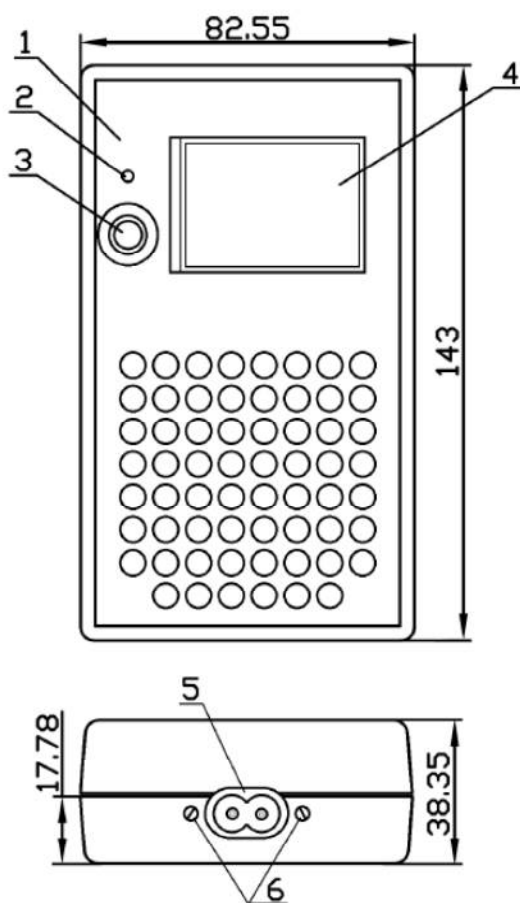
Эскиз корпуса макета под изготовление на стенке с ЧПУ.
